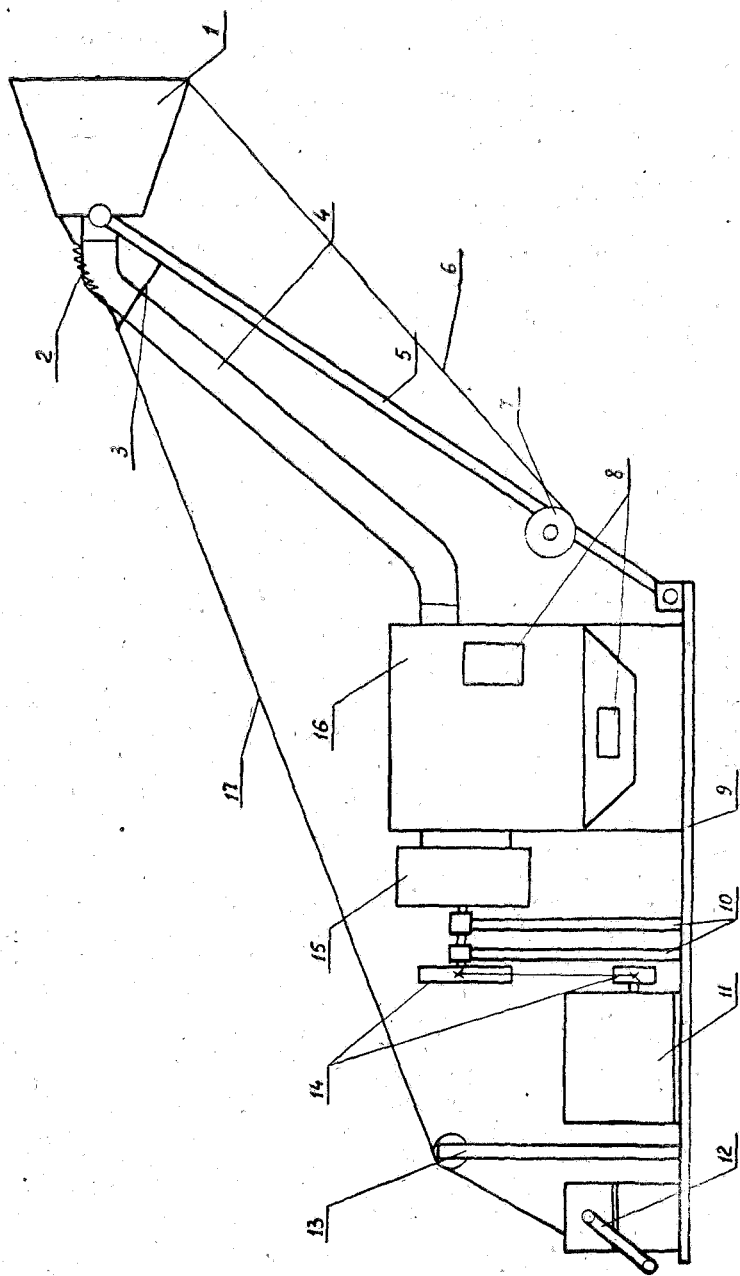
Общий вид пневмовиброустановки: 1 — сборник; 2 — подвеска; 3 — стойка; 4 — воздухопровод; 5 — стрела; 6 — трос вибратора; 7 — электродвигатель вибратора; 8 — окча; 9 — рама; 10 — панель; 11 — переключатель; 12 — основание; 13 — ножка; 14 — ножка; 15 — электродвигатель; 16 — корпус вибратора; 17 — указатель.
